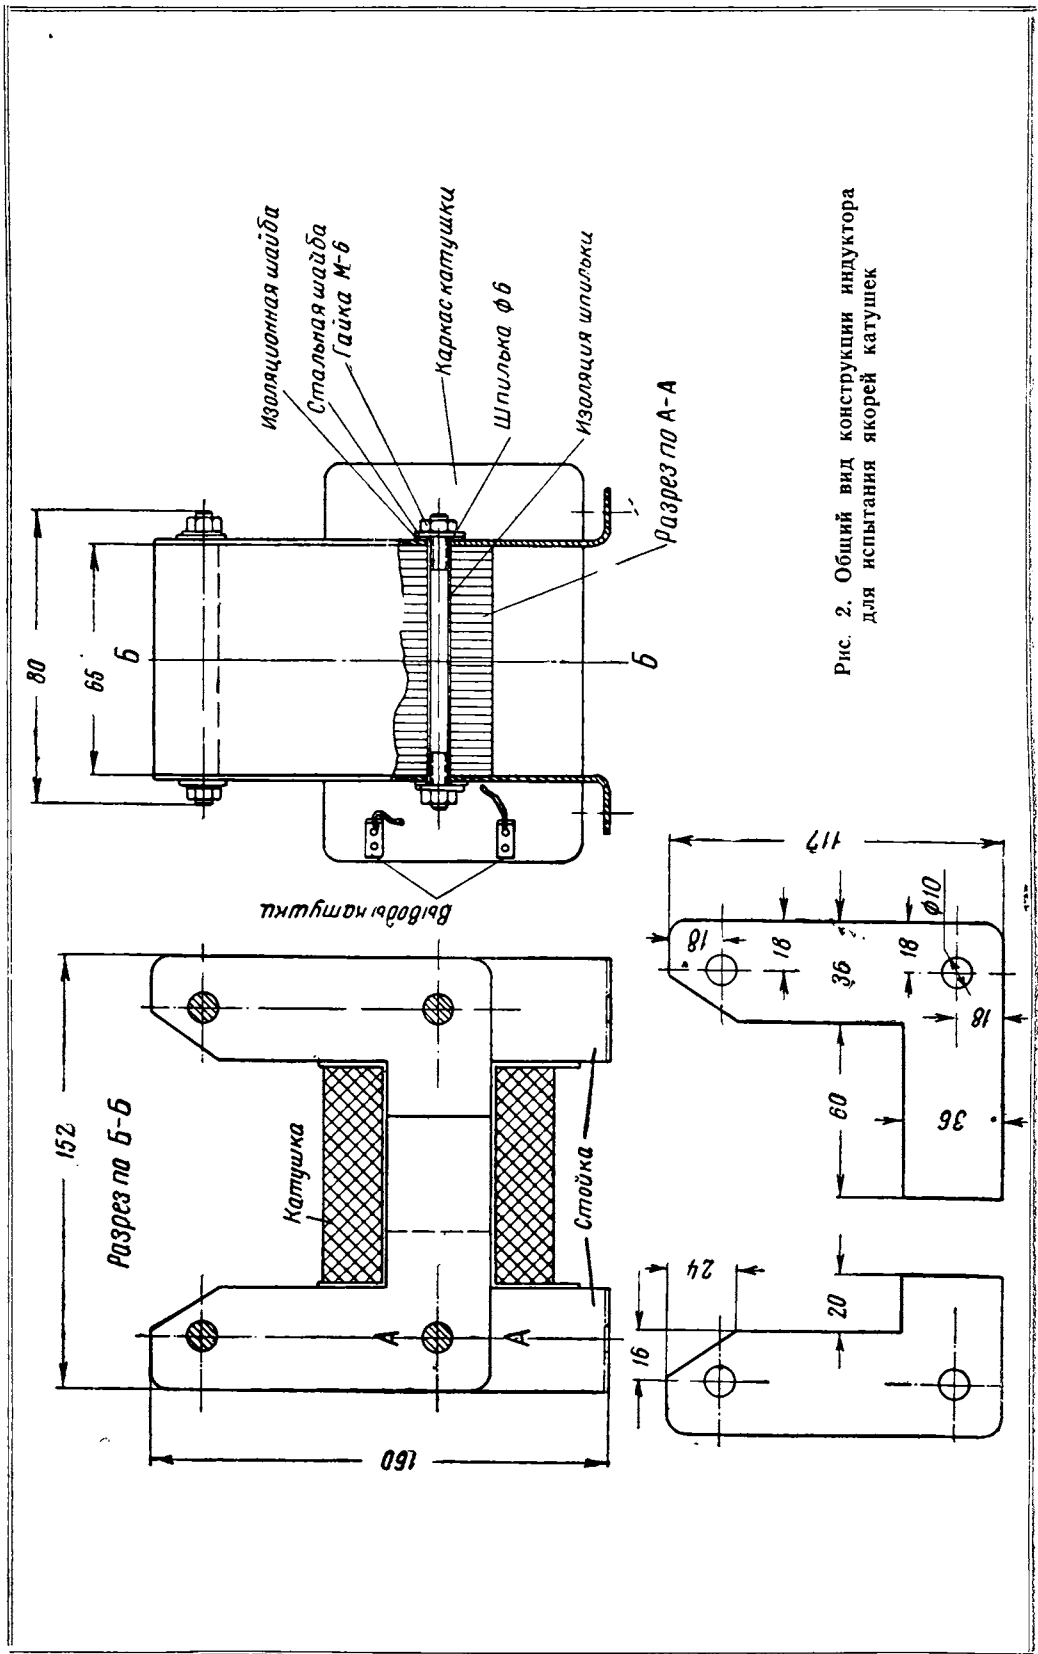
Общий вид конструкции индуктора для испытания якорей катушек
